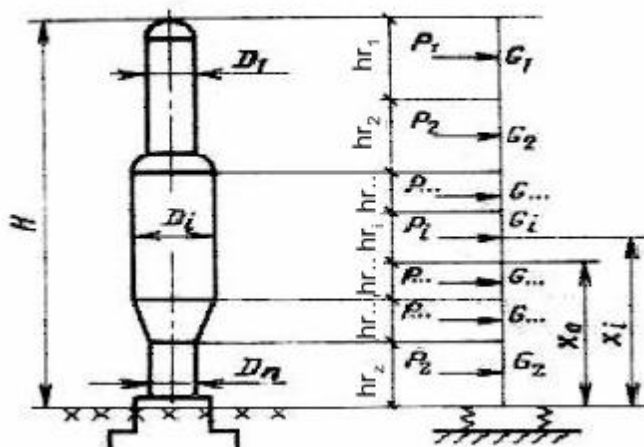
Схема разбивки аппарата на участки при расчете его на ветровую нагрузку.
